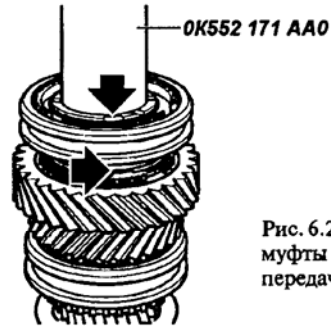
Установка ступицы и муфты синхронизатора 1 и 2 передачи
